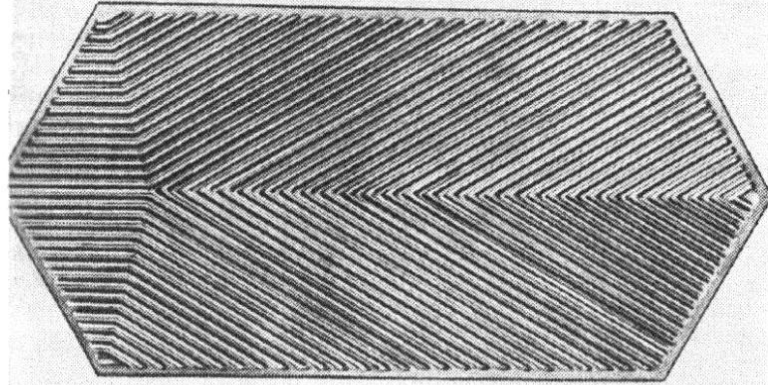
Пластина ПС-0,8 для блочных сварных теплообменников
